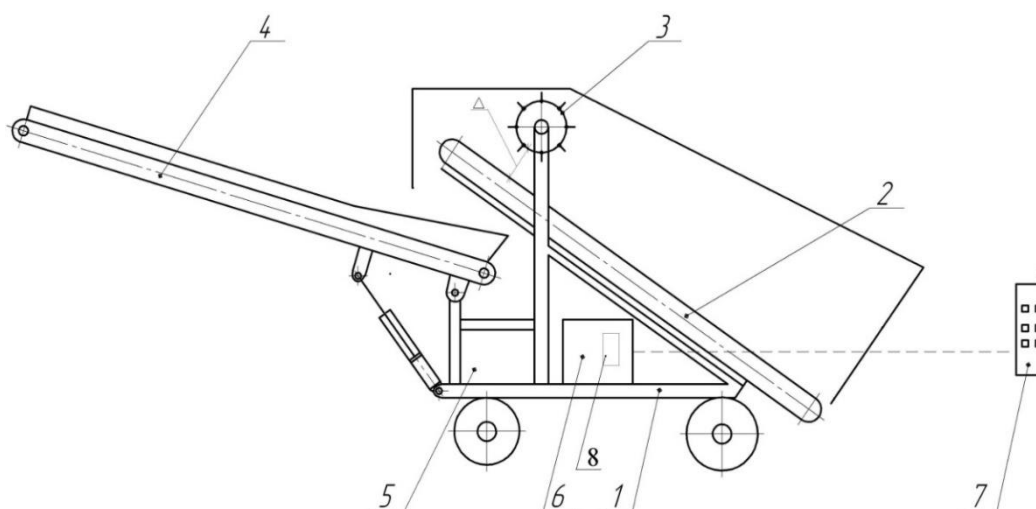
Компоновочная схема машины для приготовления компоста
